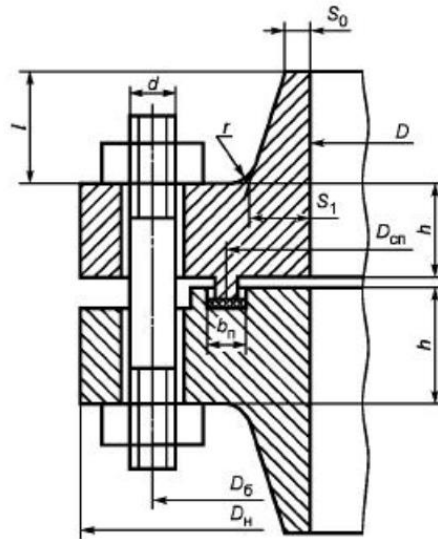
Фланцевое соединение с уплотнительной поверхностью шип-паз
